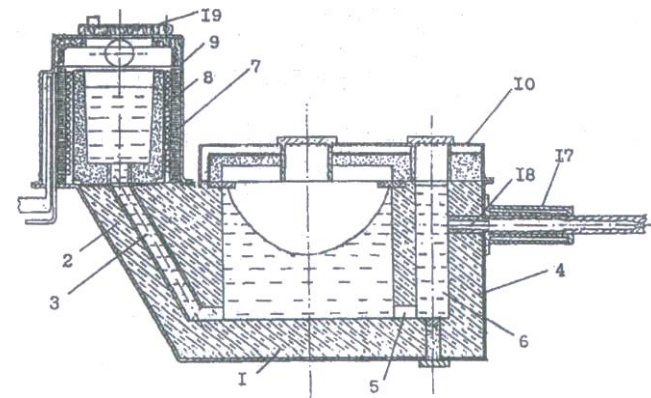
Агрегат подготовки жидкого металла к разливке; 1 - футерованная камера; 2 - блок подвода расплава в камеру; 3 - металлопровод; 4 - блок передачи металла в литейную камеру; 5 - металлопровод; 6- дополнительная литейная камера; 7 - вакуумно-индукционная печь; 8 - тигель; 9 - герметичный корпус; 10 - крышка; 11 - МГД-устройство; 17 - кристаллизатор; 18 - сливная летка; 19 - крышка тигельной печи
